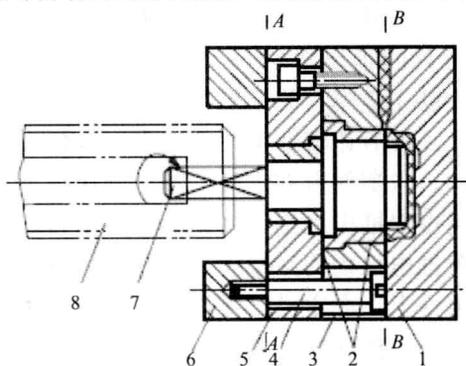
用于直角式注塑机的自动卸螺纹注塑模具
